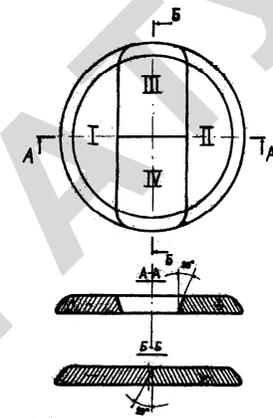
Пресс-форма приспособления для правки крышек ведер
